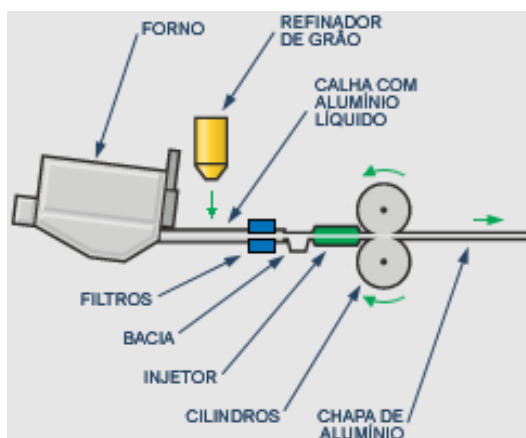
Processo de fabricação das bobinas de caster (material da empresa)
